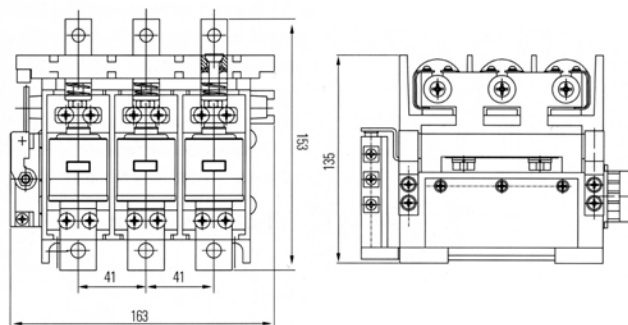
Габаритные размеры КВТ-1,14-80/125/160
